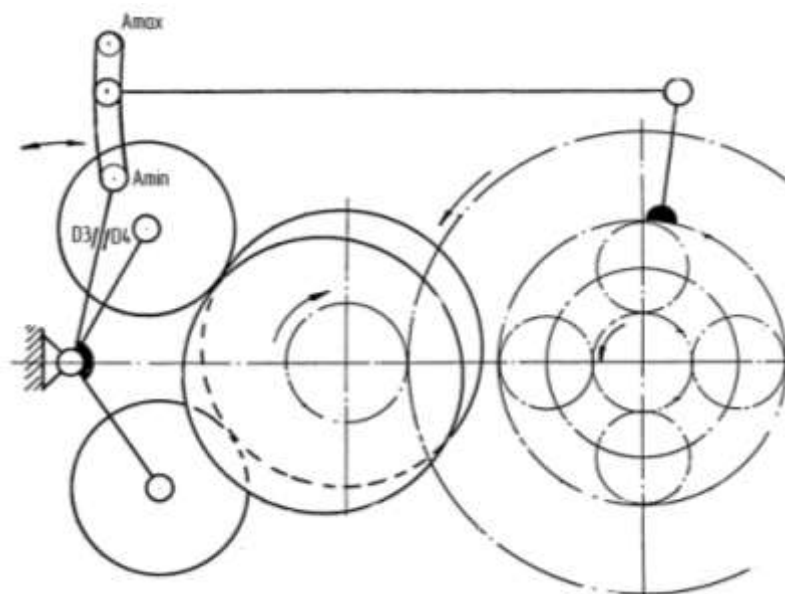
Схема установки датчиков на коромысле кулачкового механизма привода каретки
